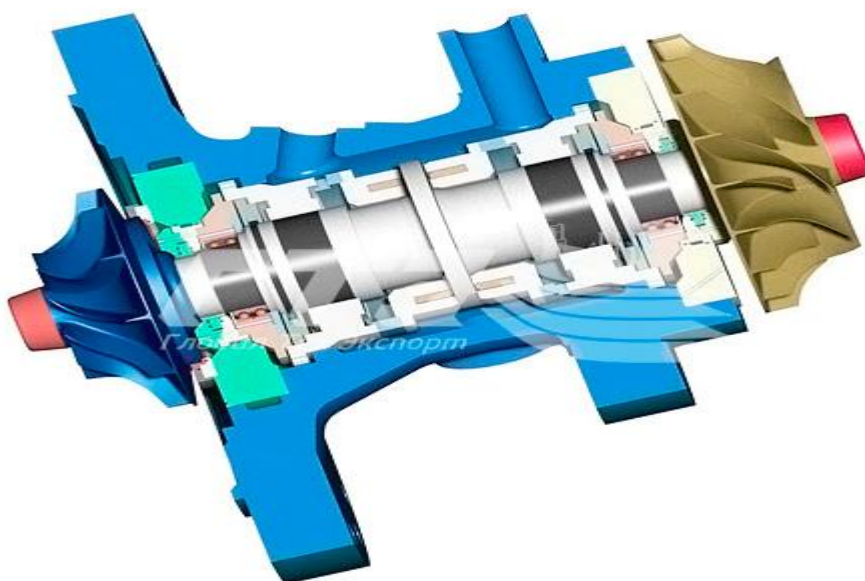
Магнитный радиальный подшипник (разрез модуля)
